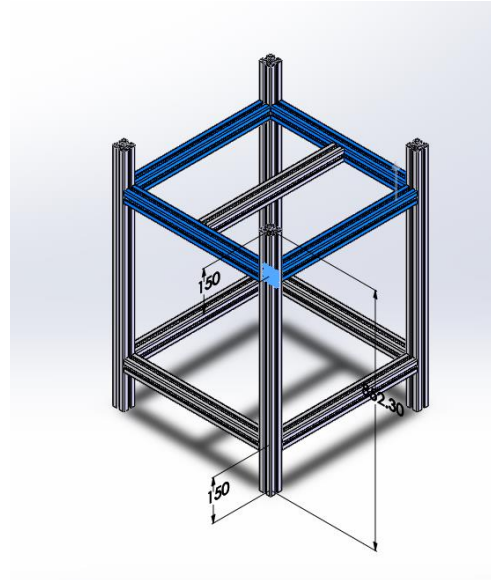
Extrusión del sketch 3D para generar el solido de la bancada
